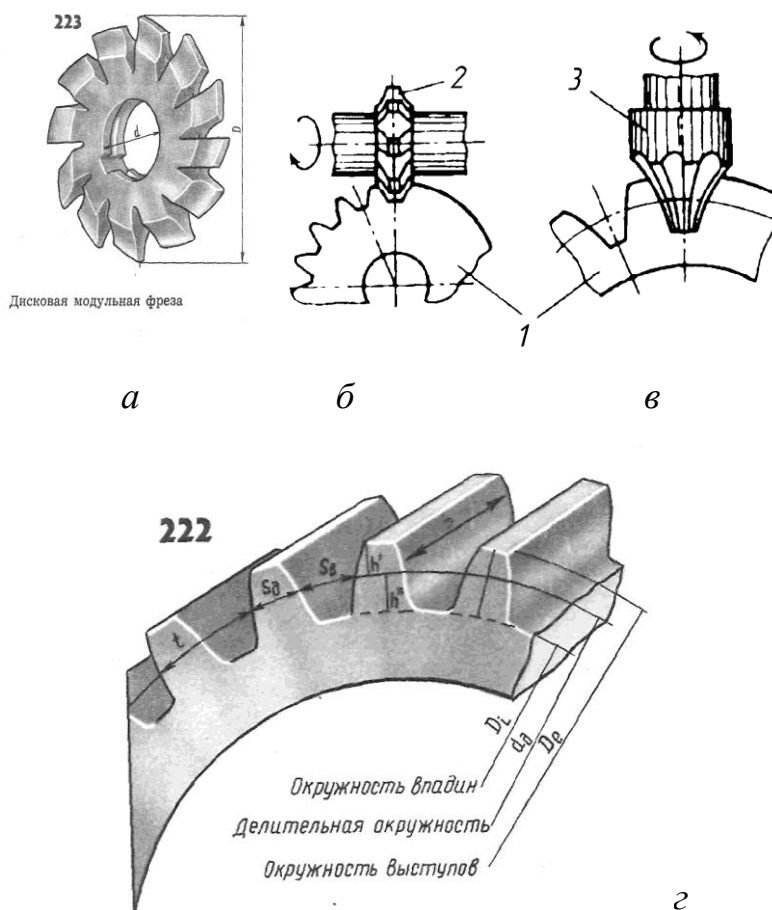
Нарезание зубьев зубчатых колес по методу копирования фрезерованием:
